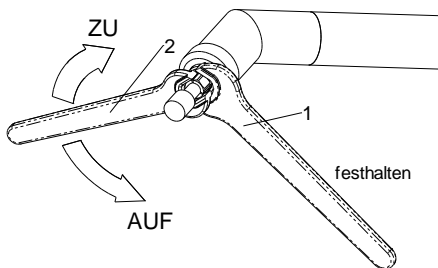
Werkzeugwechsel Spannzange ZG 4/6
